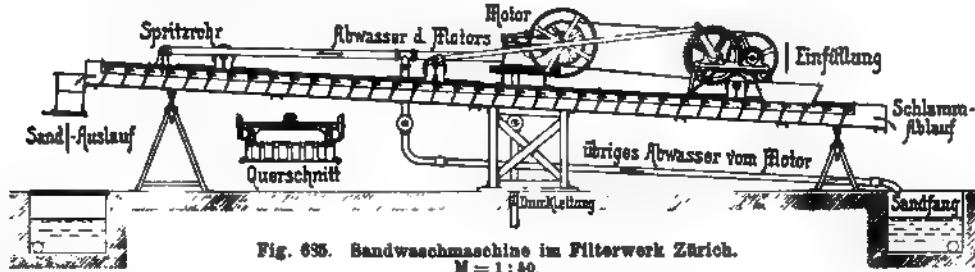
Sandwaschmaschine im Filterwerk Zürich.
